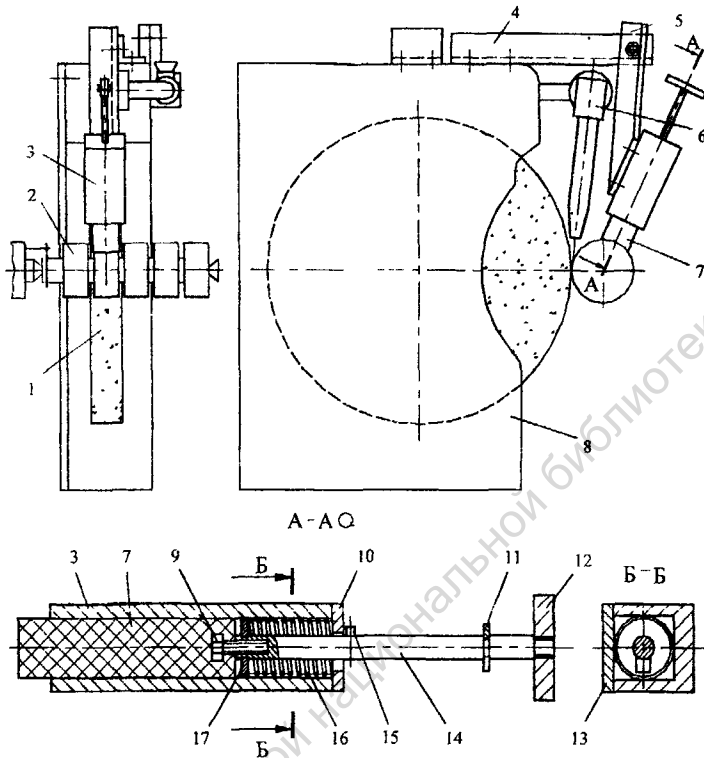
Экспериментальная установка для поэтапной подачи СОТС: 1 – шлифовальный круг; 2 – заготовка; 3 – корпус; 4, 5 – кронштейны; 6 – сопло для подачи водной СОЖ; 7 – брикет ТСМ; 8 – защитный кожух; 9 – болт; 10 – крышка; 11 – шайба; 12 – рукоятка; 13 – крышка; 14 – шток; 15 – штифт; 16 – пружина; 17 – шайба
